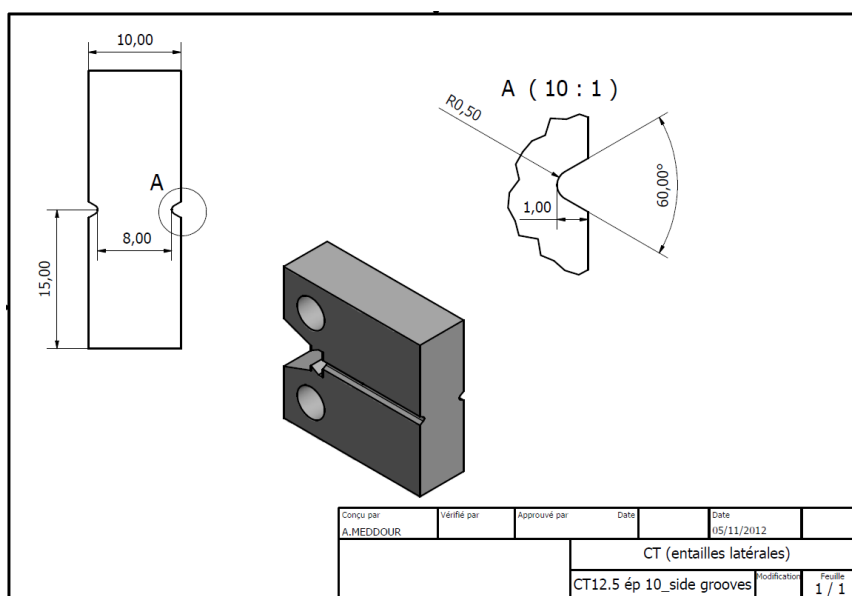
Plan d'usinage des éprouvettes de ténacité CT12.5
